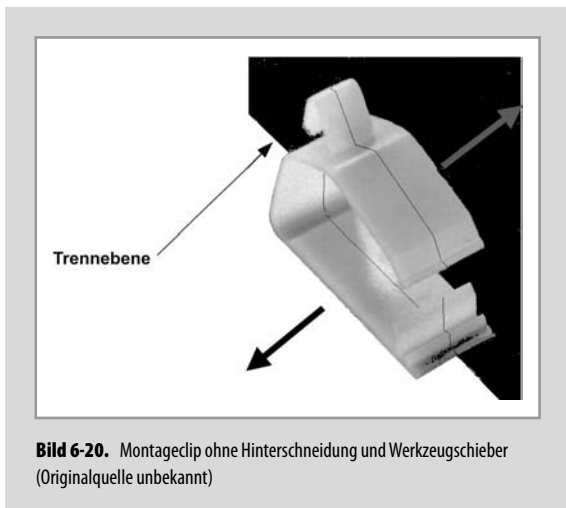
Montageclip ohne Hinterschneidung und Werkzeugschieber (Originalquelle unbekannt)
